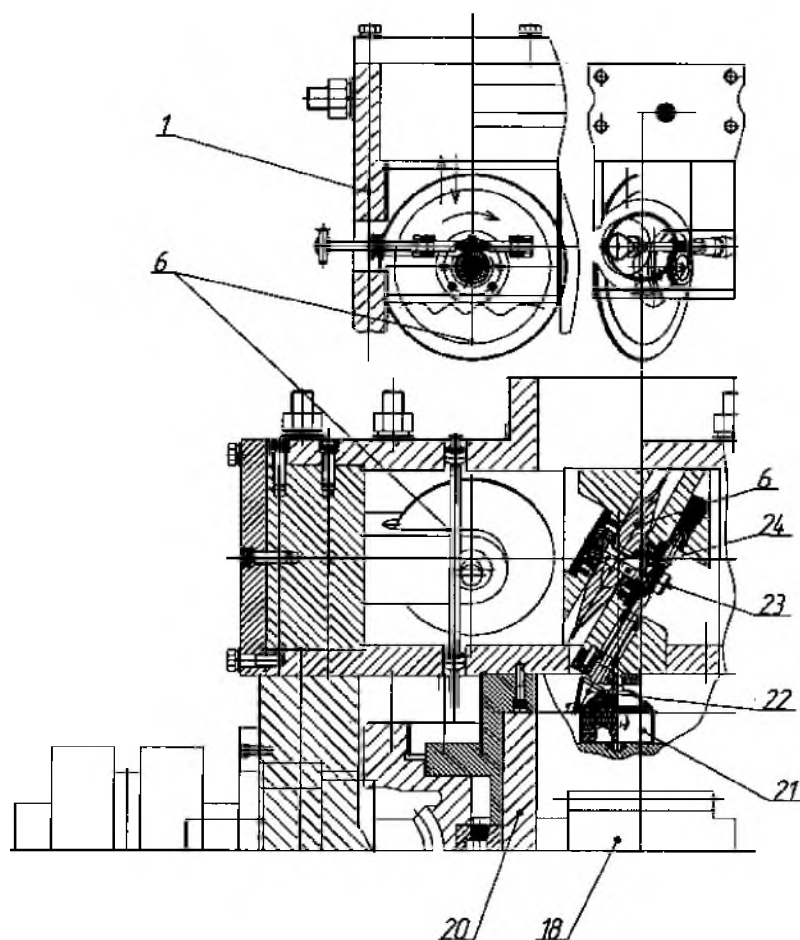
Схема крепления ролика: 1 – клеть; 6 – ролик; 18 – червячный вал; 20 – ротор; 21 – шестерня; 22 – косозубые шестерни; 23 – червячный вал; 24 – червячное колесо (23–24, модуль $m=2$ мм)
